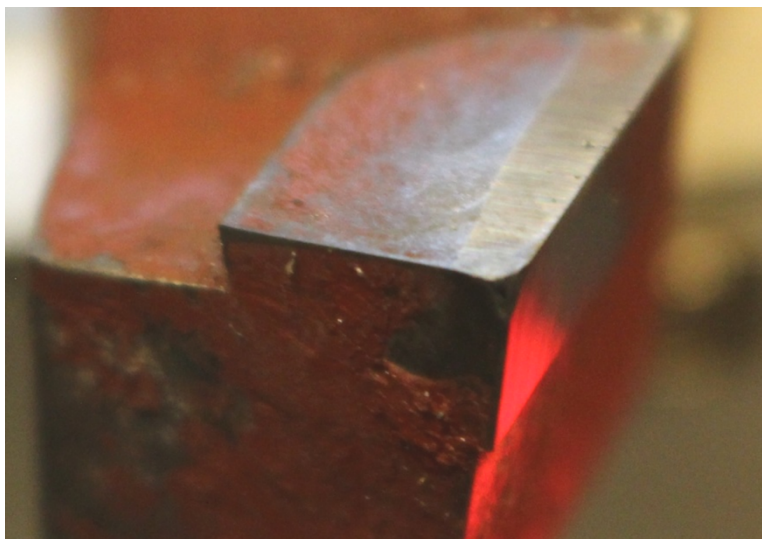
Řezný nástroj obrábějící tvrdý materiál, zdroj: autor
